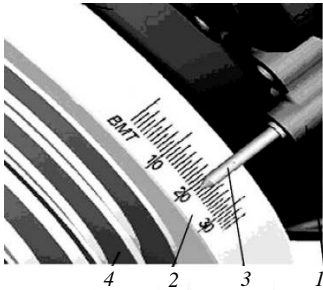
Установка угла опережения впрыска топлива двигателя Д-260:
